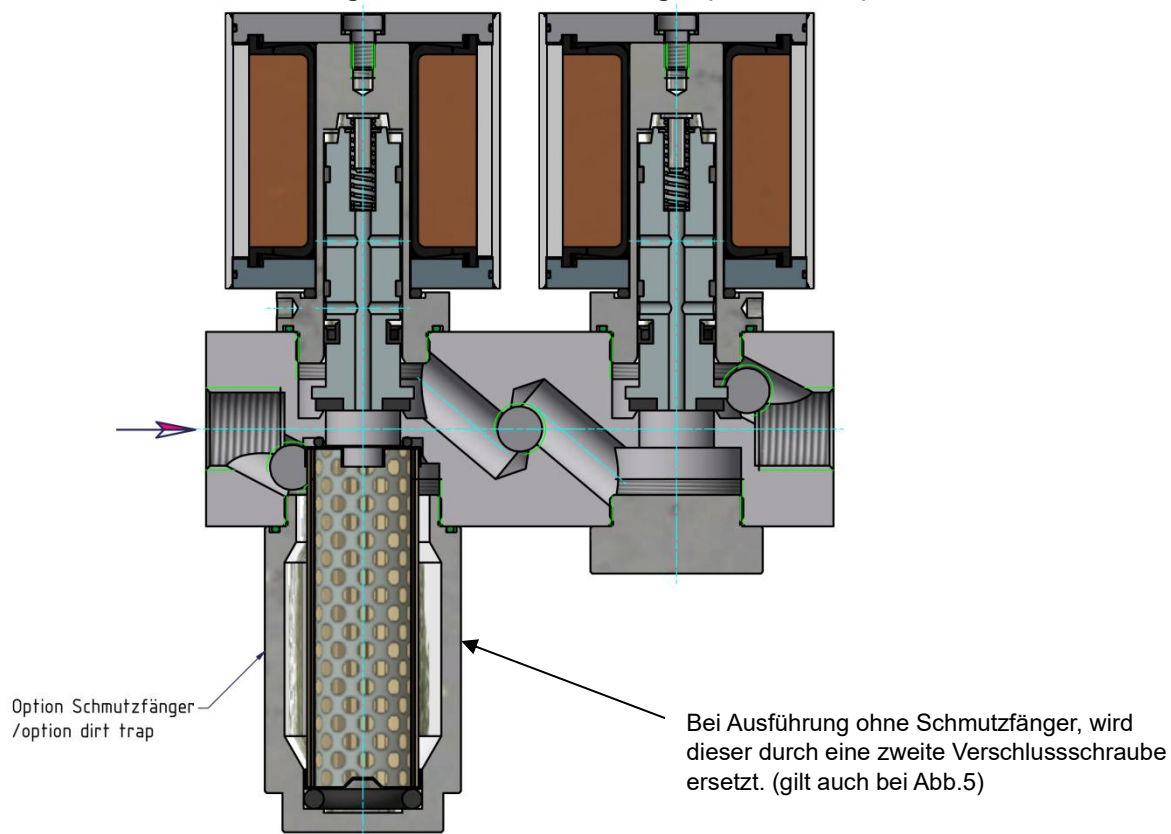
Gewindeausführung DVS... mit Schmutzfänger (116.002.295)
